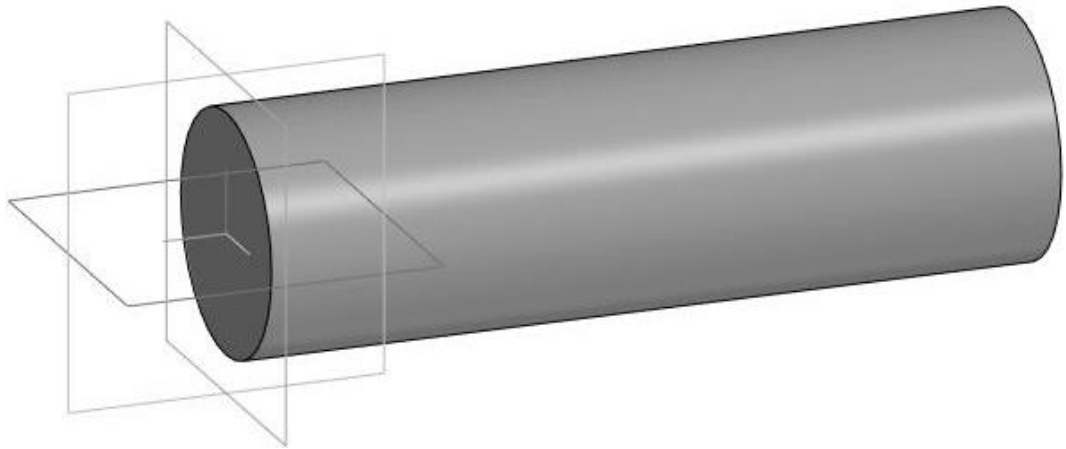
3D модель заготівки з прутка, для розрахунку маси у NX
